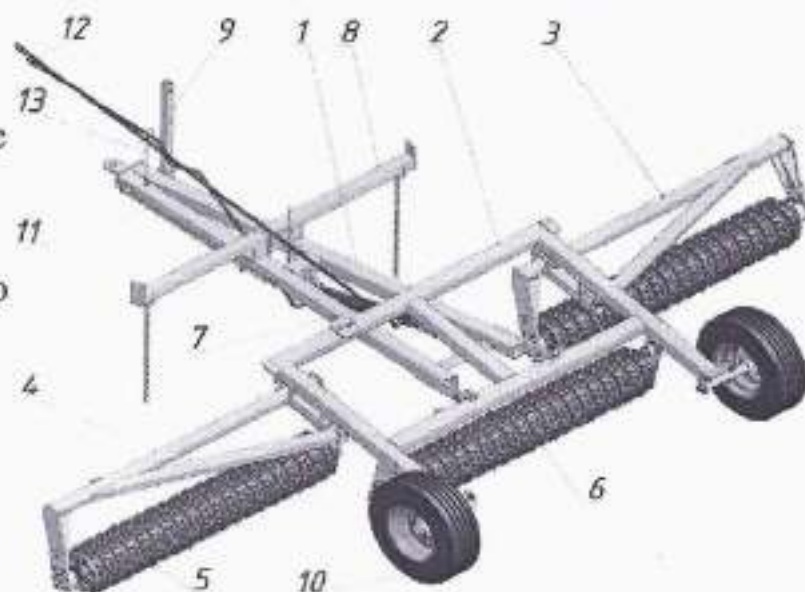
Каток кольчато-зубчатый ККЗ-6 в рабочем положении
